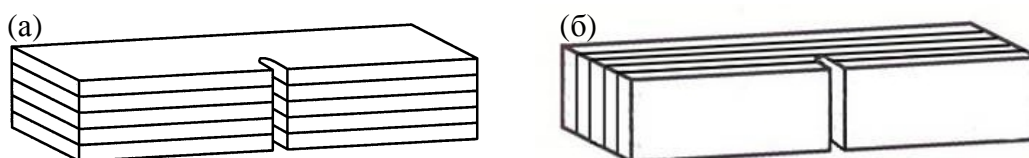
Образец для испытаний на ударный изгиб с «разветвляющим» (а) и «тормозящим» (б) трещину расположением поверхностей соединения
